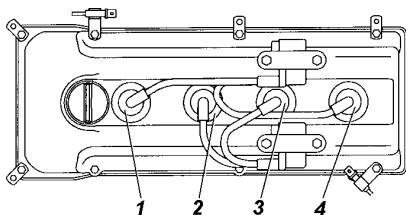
Порядок установки высоковольтных проводов двигателя 3МЗ-409:
